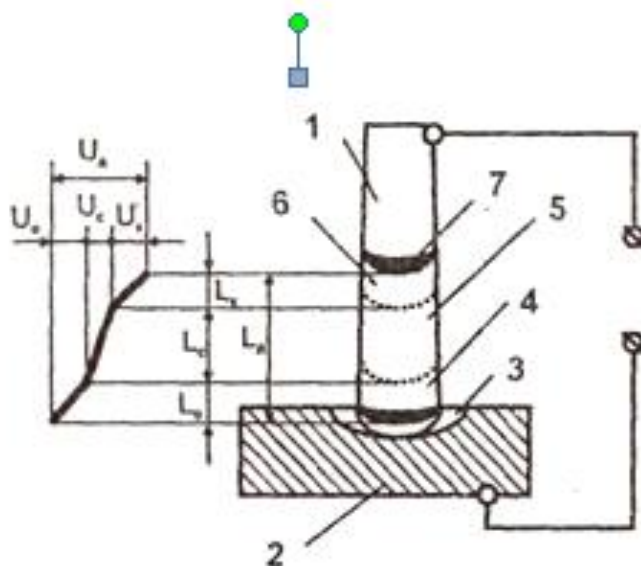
Схема сварочной дуги и падения напряжений в ней:
